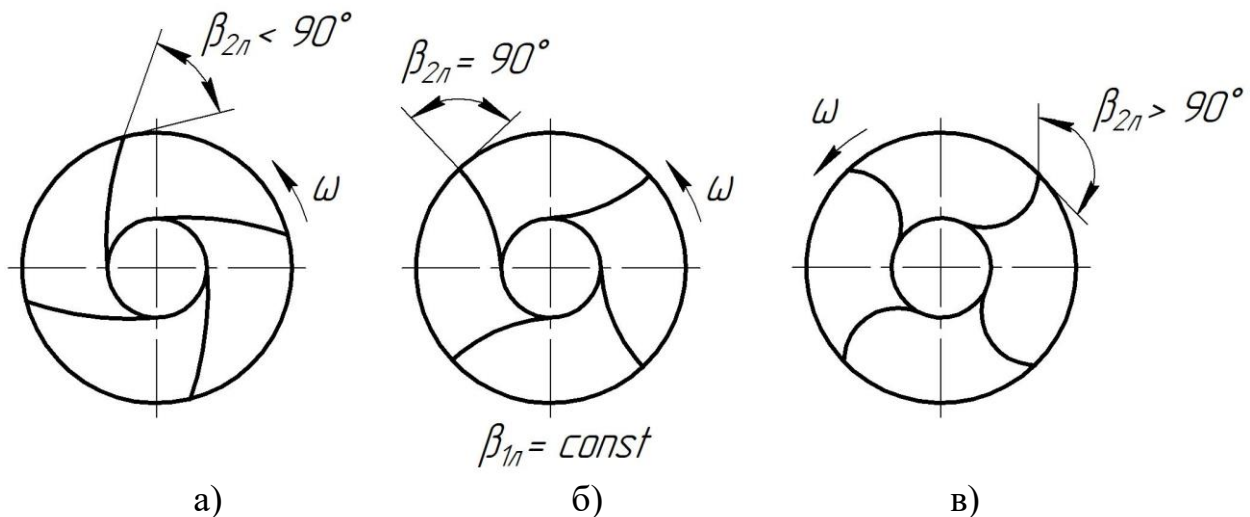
Схеми робочих коліс із різними кутами лопатей на виході з робочого колеса
